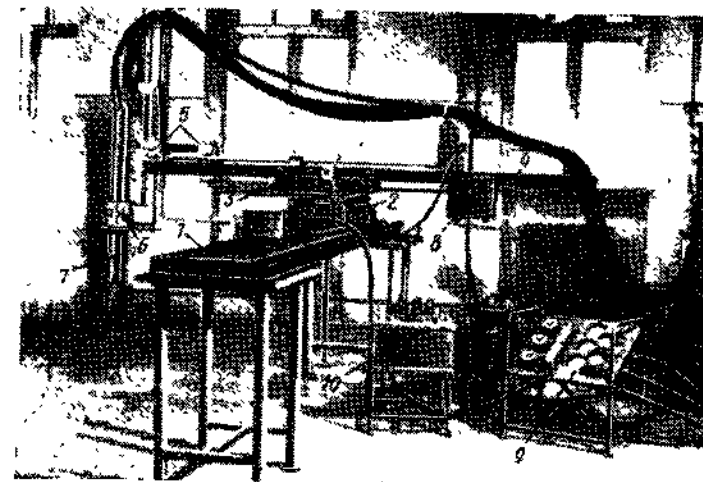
Установка ПМР-1000 для резки стали больших толщин:
